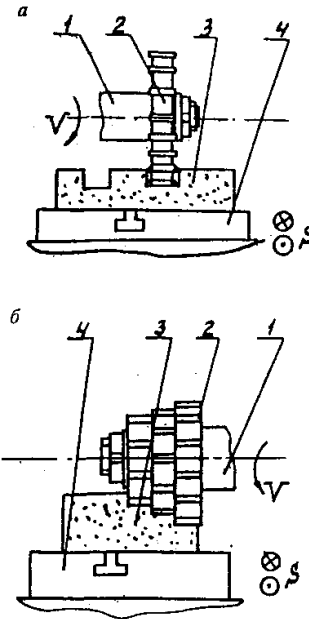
Схемы обработки камня цилиндрическими алмазными фрезами: а — обработка пазов; б — обработка ступенчатых поверхностей набором фрез различных диаметров; 1 — шпиндель; 2 — набор цилиндрических алмазных фрез; 3 — обрабатываемая заготовка; 4 — стол станка; V — вращательное движение резания; S — рабочая подача стола
